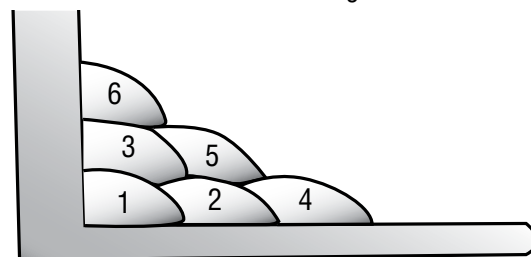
Múltiplo passe na solda horizontal em ângulo
